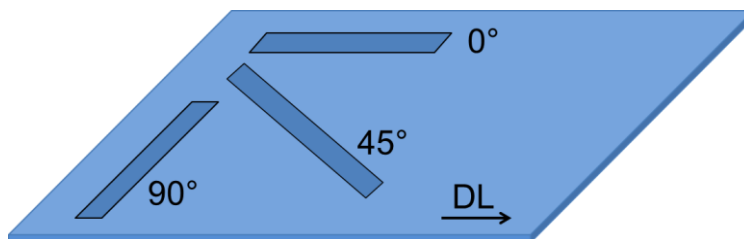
Illustration des directions du découpage des éprouvettes
